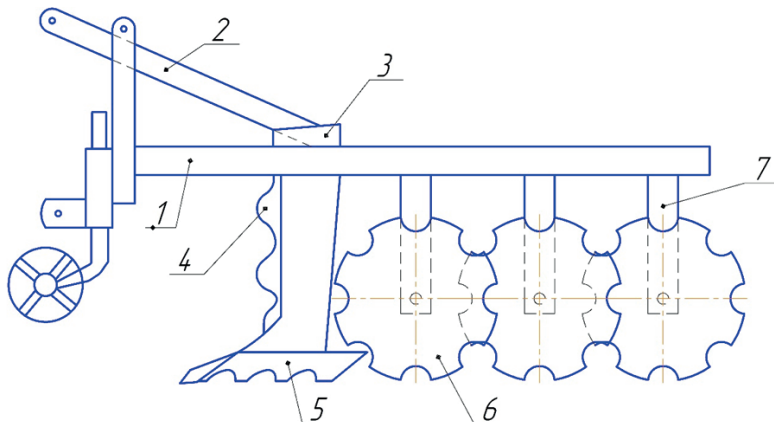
Схема зубчато-дискового плуга для укрывки виноградников
